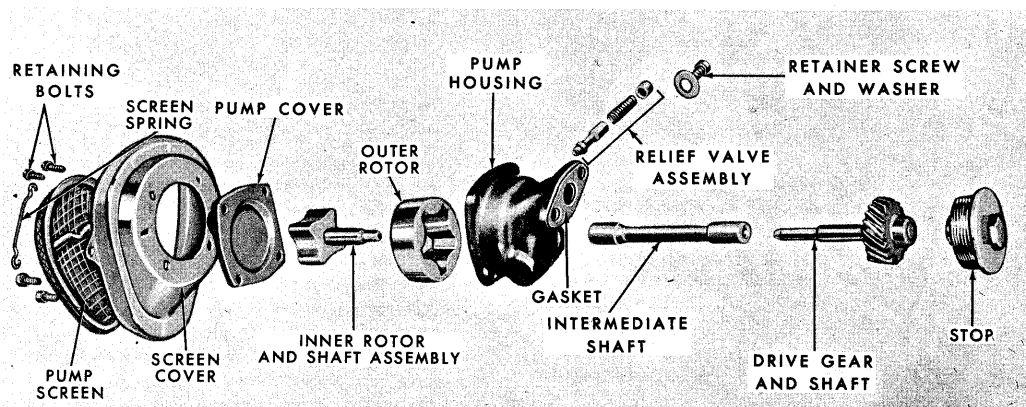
Exploded view af oliepumpen med si, reduktionsventil, aksel og drev.
